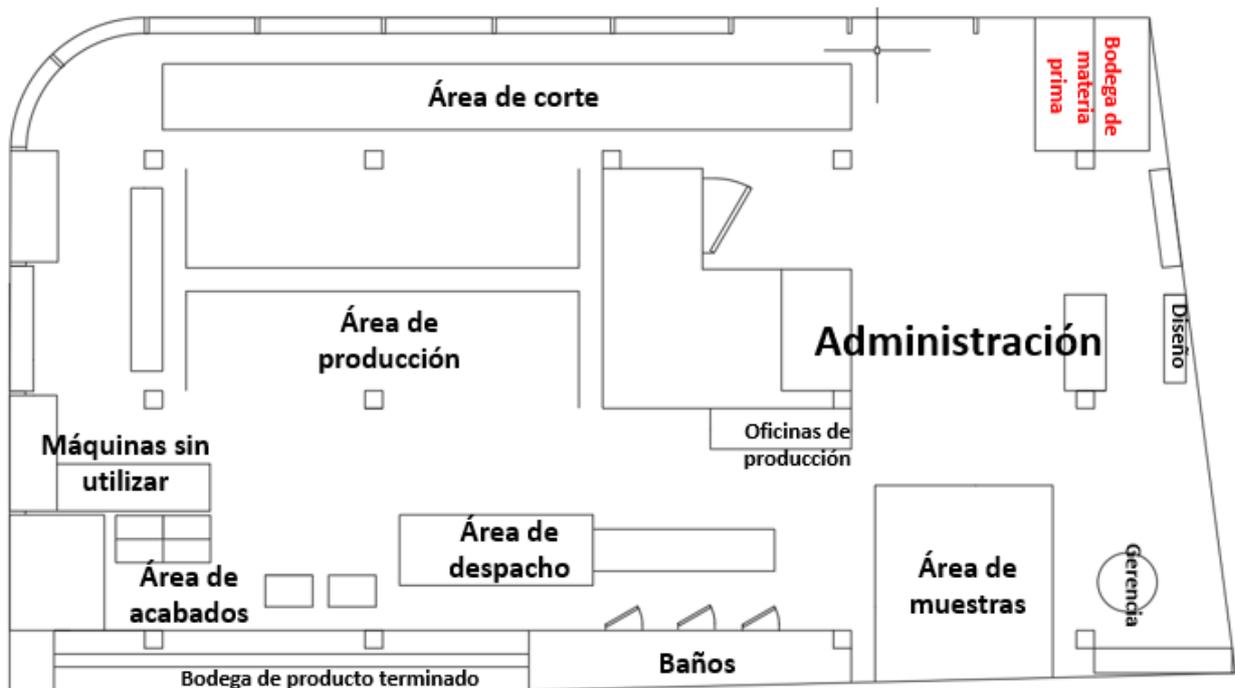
Layout de la situación actual. fuente: Elaboración propia
